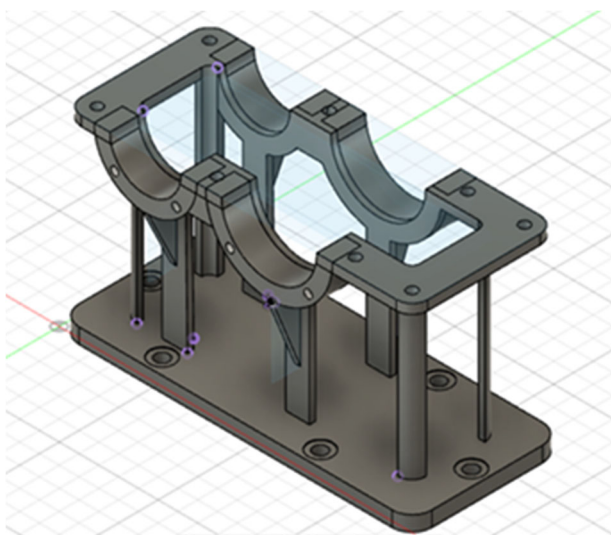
Корпус одноступеневого редуктора з видаленими ненавантаженими ділянками
